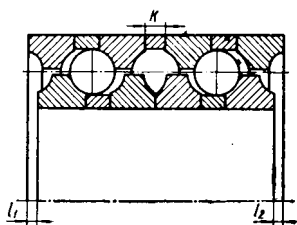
Схема сборки работоспособного подшипника из отработанных.
